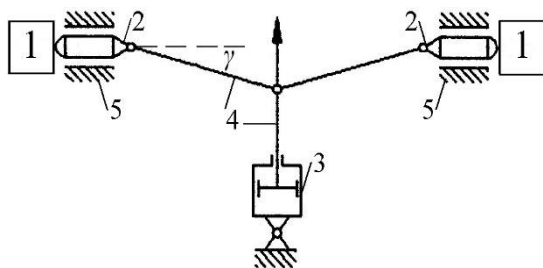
Схема нагружения в маложесткого кольца 1 плунжерами 2 в устройстве по патенту [3], 3 – гидропривод, 4 – рычажно-шарнирный механизм, 5 – корпус, γ – угол наклона рычага
